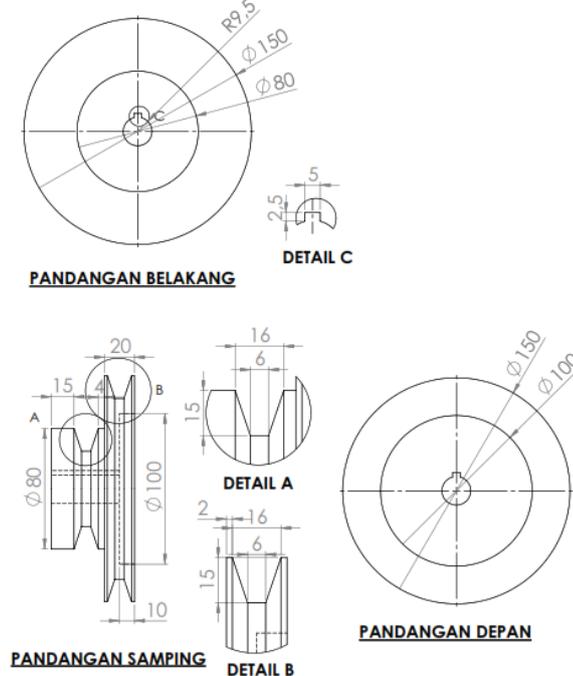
Drawing *Pulley Hammer Mill
